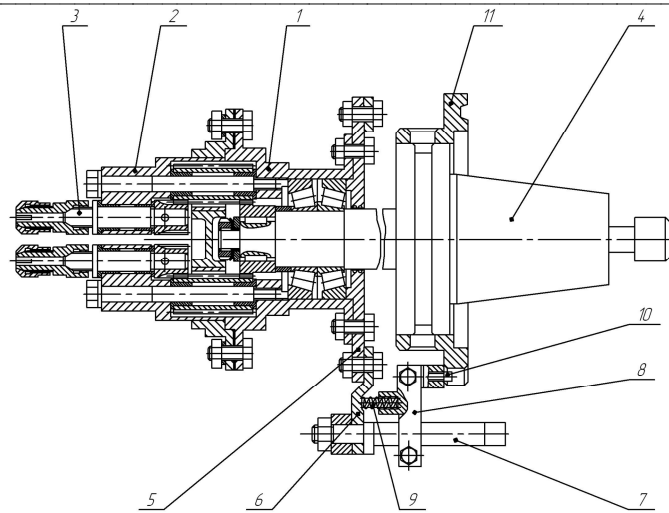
Багатошпindelна головка для верстата з ЧПК
